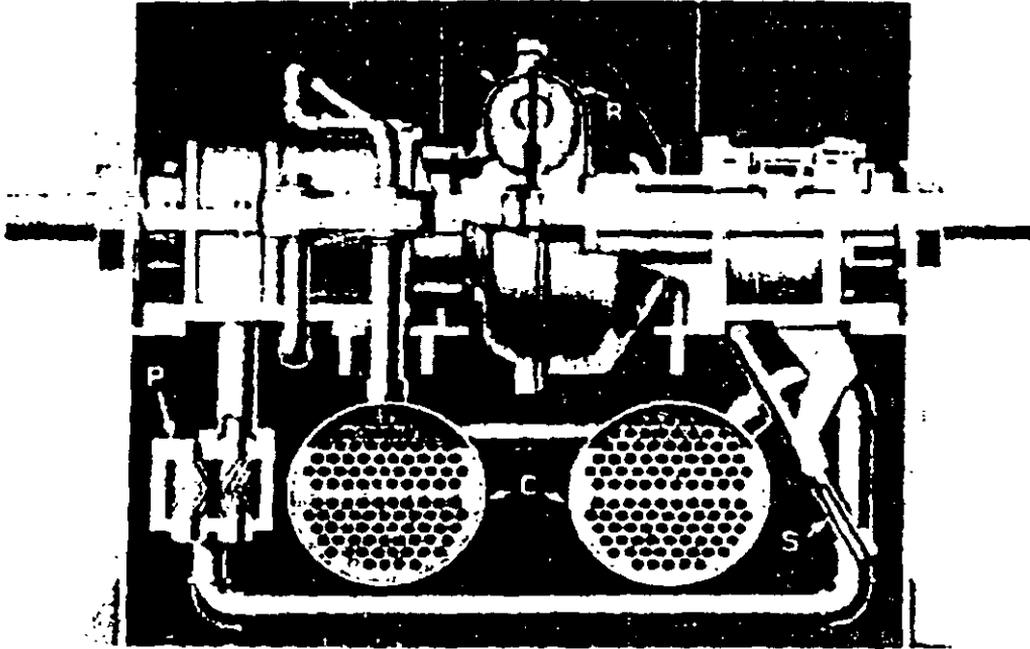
Transmisión hidráulica para paliación de bomba (Cortesía de American Blower Corp.)
